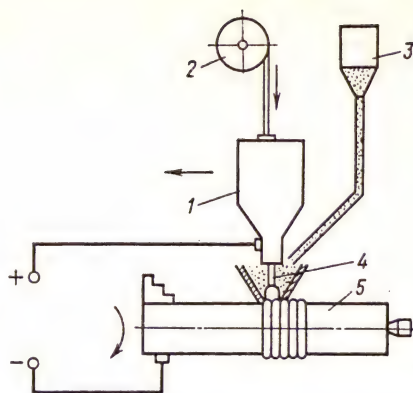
Схема установки для автоматической наплавки под флюсом:
